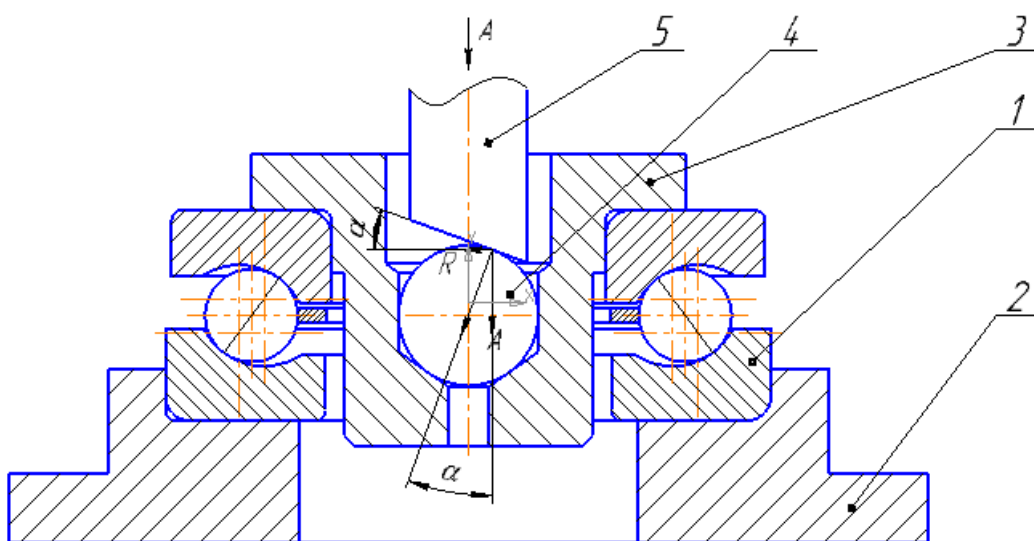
Конструкция устройства для определения статической грузоподъемности упорно-радиального шарикоподшипника при комбинированной нагрузке: 1 – измеряемый подшипник; 2 – основание; 3 – оправка; 4 – шар; 5 – упор.
